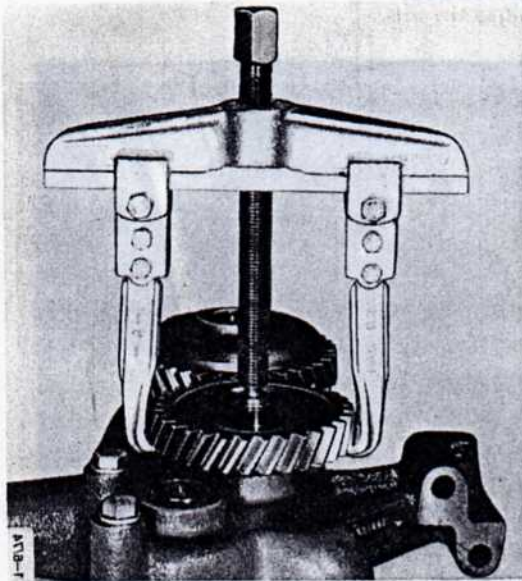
Sacar el engranaje motriz de la bomba de aceite
